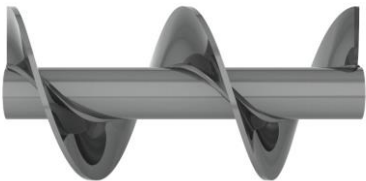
Типовий вертикальний гвинтовий конвеєр фірми KWS [215]
